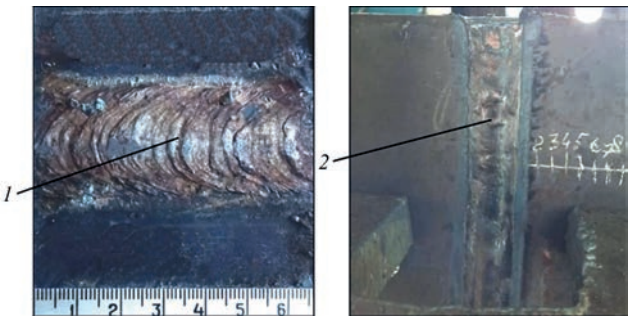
Зовнішній вигляд зварних швів, виконаних зварюванням з примусовим формуванням: 1, 2 – зварені зразки заготовшки 12 і 20 мм відповідно
